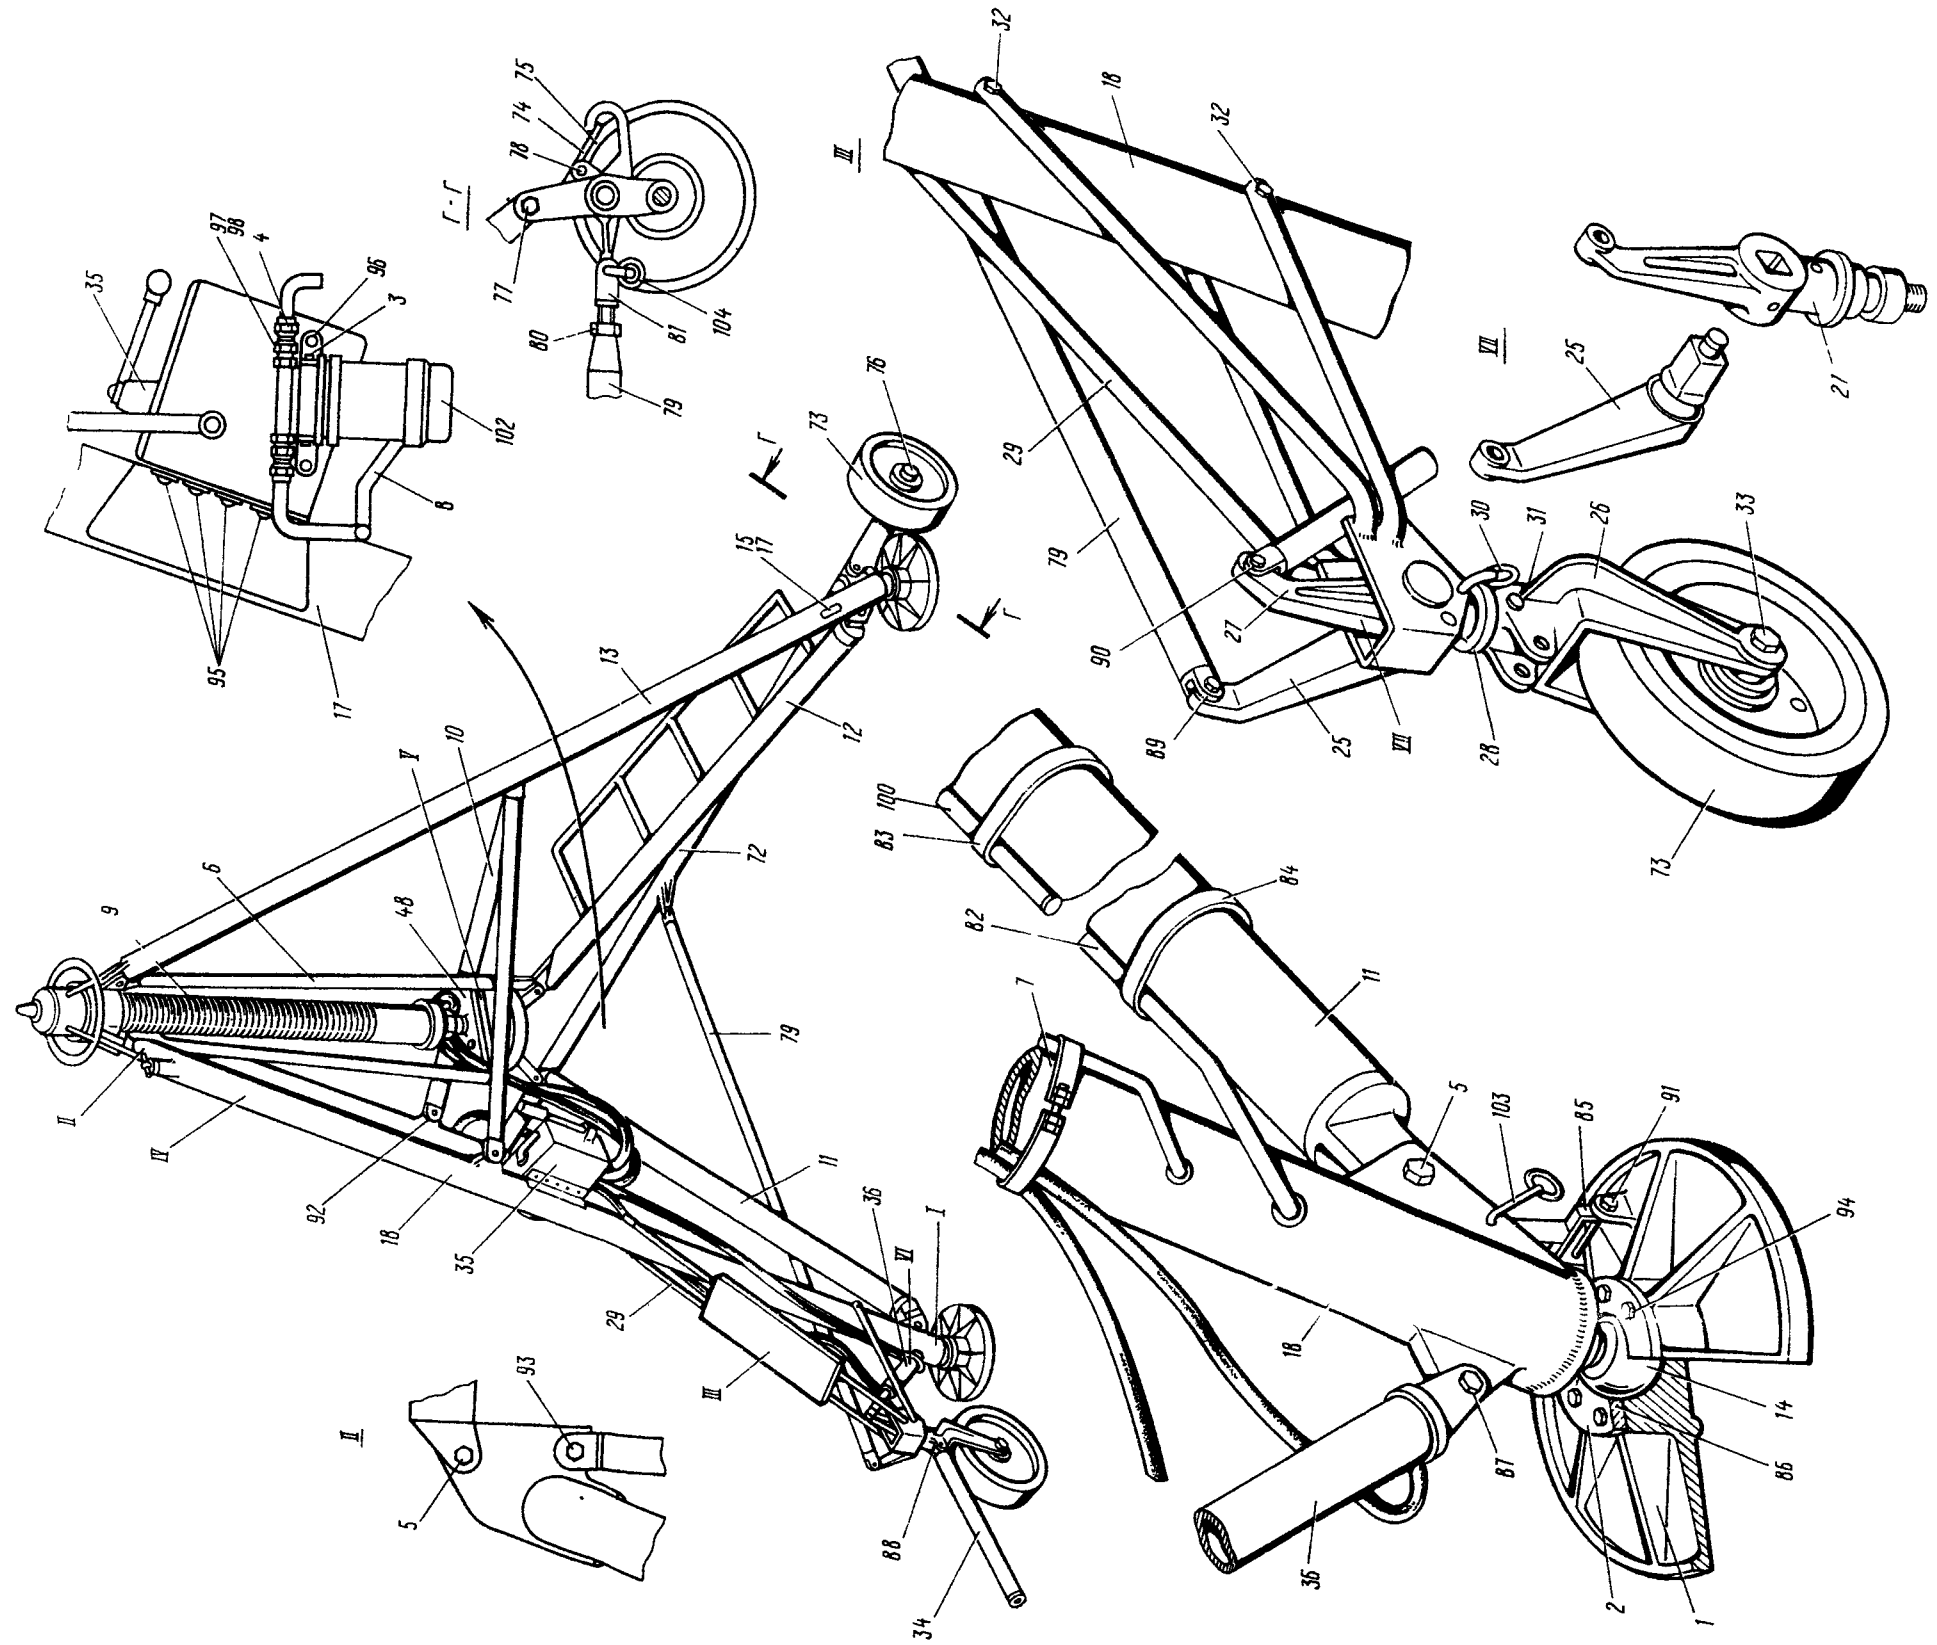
ГИДРОПОДЪЕМНИК ГЛАВНЫЙ (ЛИСТ I)
